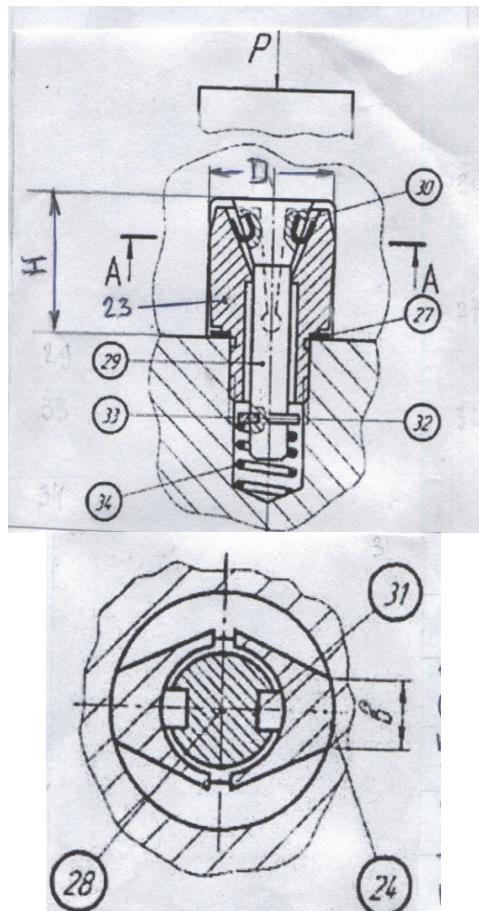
Схема установки заготовки (пат. 2390400) корпусной заготовки на отверстия (искусственные технологические базы)
